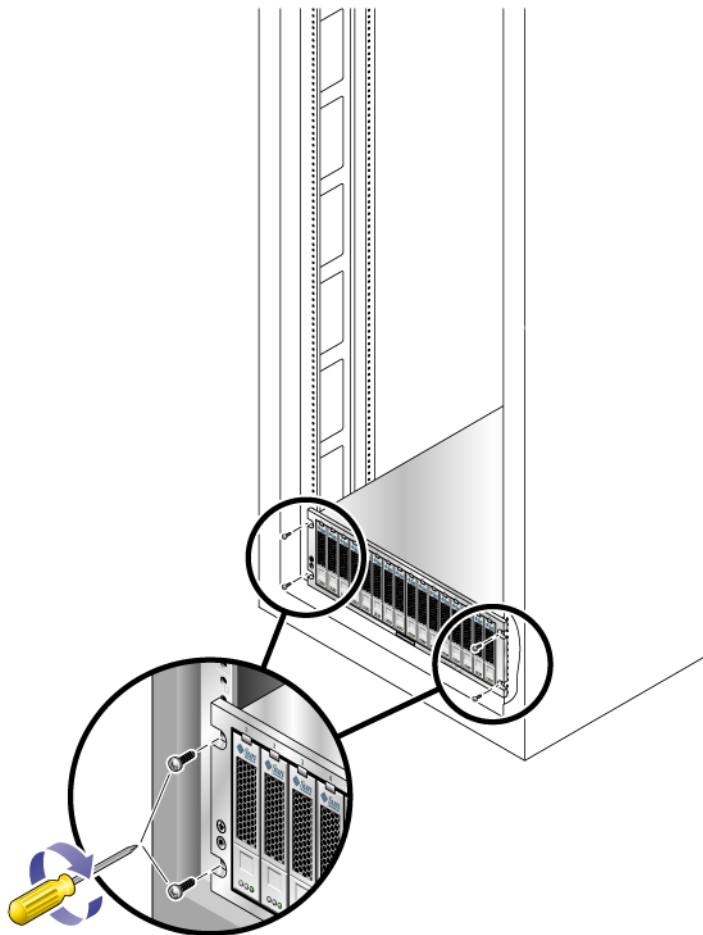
Fixation du plateau à l'avant d'une armoire Sun StorEdge Expansion
